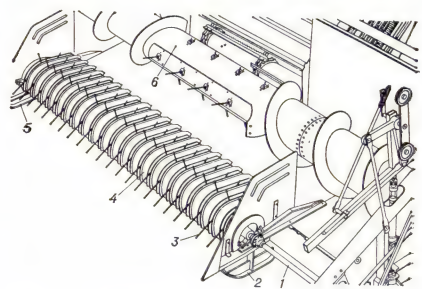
Подборщик барабанного типа: 1 — приводной вал; 2 и 5 — опорные башмаки; 3 — пружинные пальцы; 4 — цилиндрический кожух; 6 — шнековый транспортер жатки комбайна.
